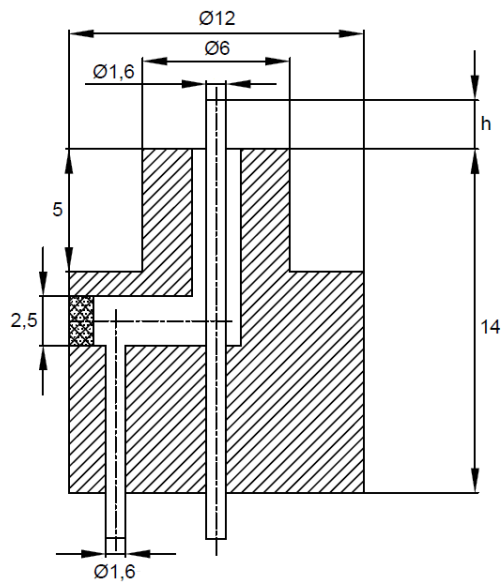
Dimensões das sondas do tipo Irwin (dimensões em mm)
